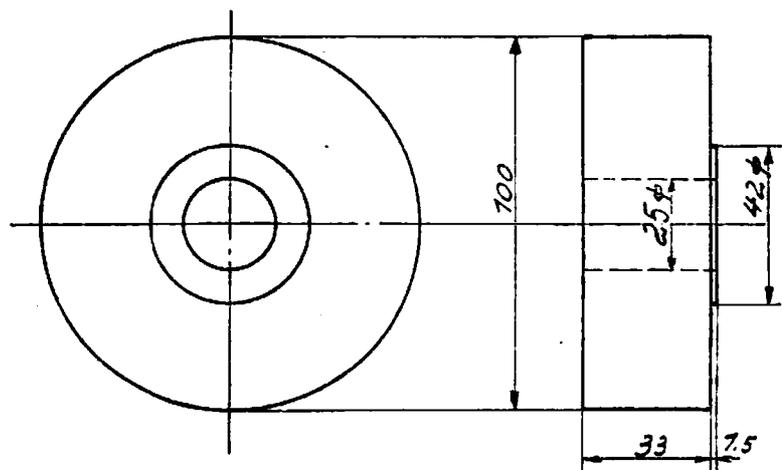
Maßskizze des Auflagestückes für die Kurbelgehäusehälften beim Eindrücken der Rollenlaufringe
